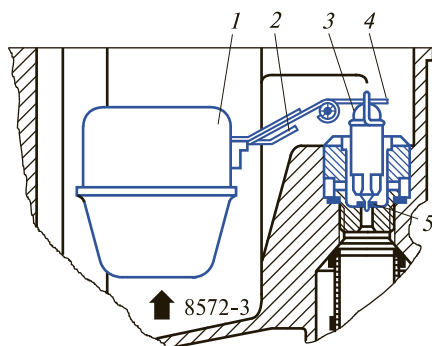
Регулировка поплавкового механизма карбюратора К-151:
